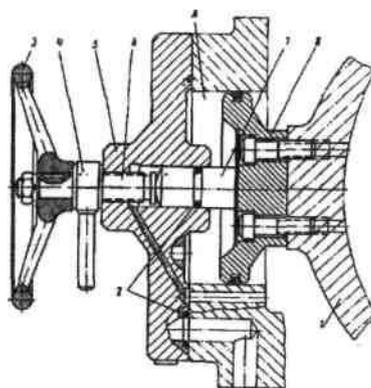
Подпорный цилиндр насосов НПМ
